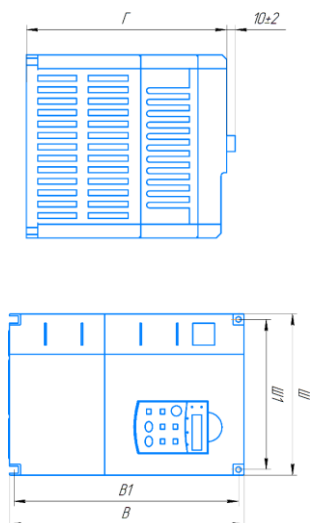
а Габаритные и установочные размеры устройств серии LCI в пластмассовом корпусе
